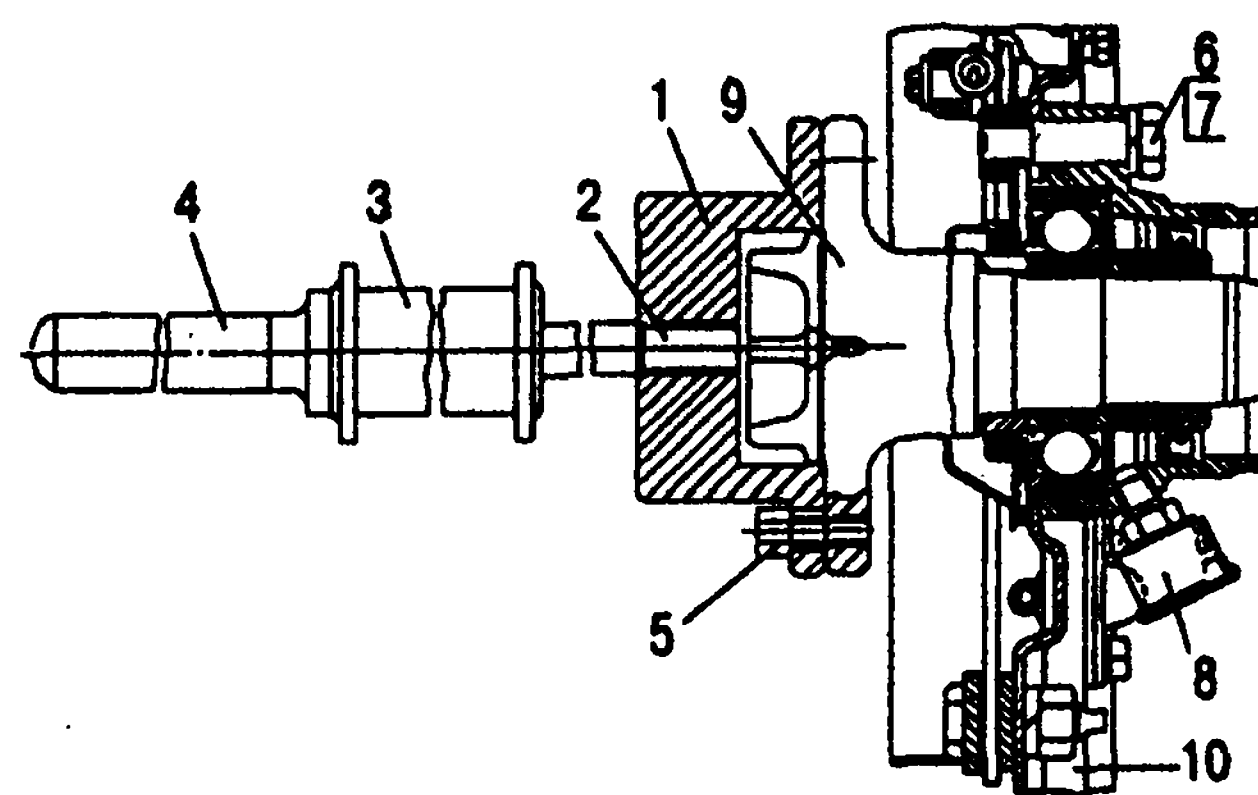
Демонтаж полуоси: 1 - фланец; 2 - шпилька; 3 - боек; 4 - ручка; 5 - болт крепления фланца к полуоси; 6 - болт крепления тормозного механизма; 7 - шайба; 8 - колпачковая масленка; 9 - полуось в сборе; 10 - тормозной механизм
